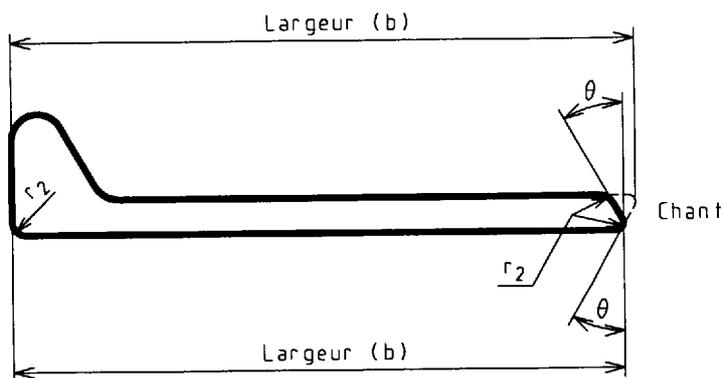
Tolérance sur le défaut d'équerrage du chant
